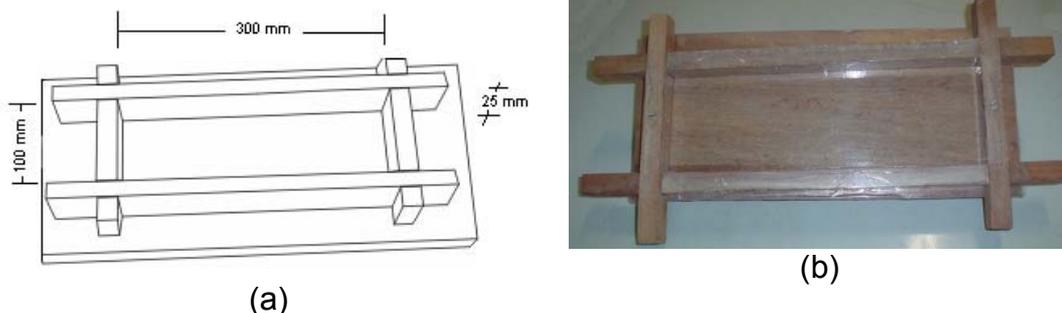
(a) Desenho esquemático do molde e (b) Molde de madeira
